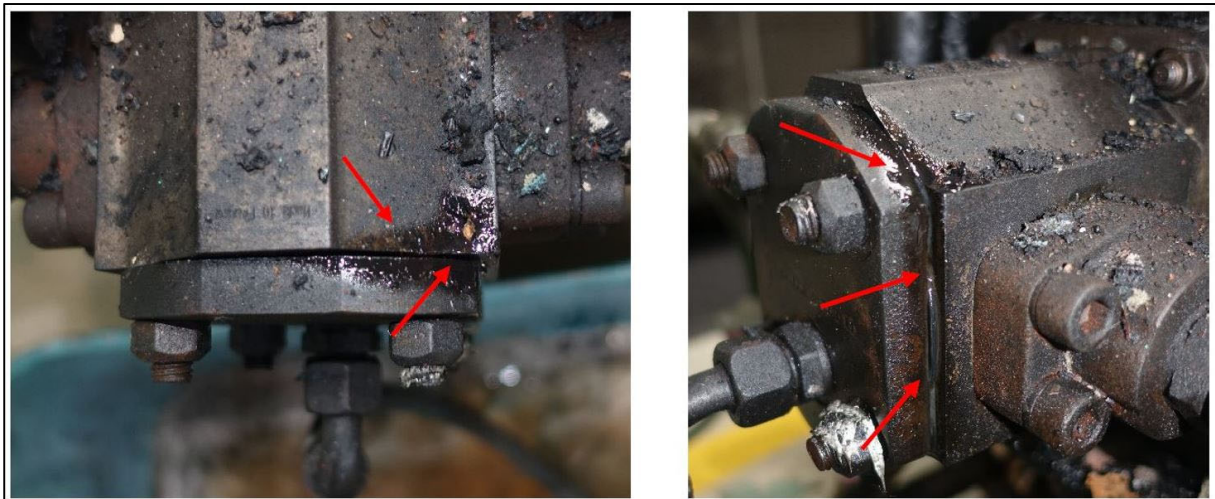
Undichter Hydrauliklüftermotor¹⁰
